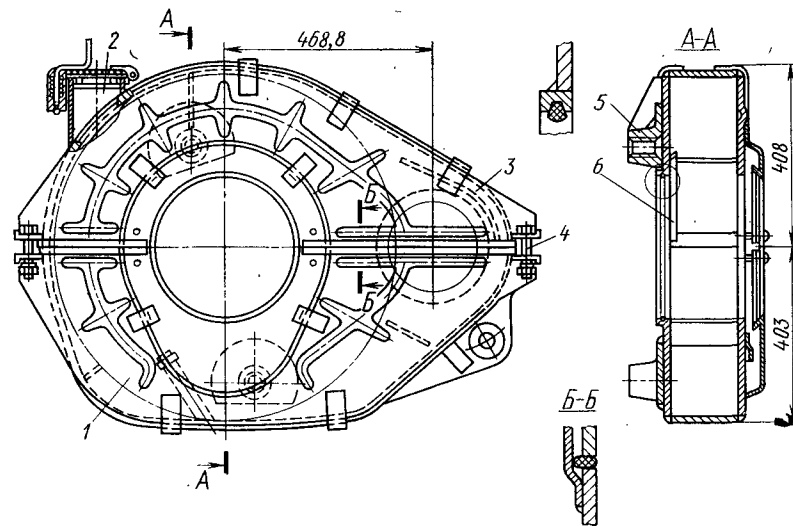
Кожух тягового редуктора тепловоза 2ТЭ10Л:
